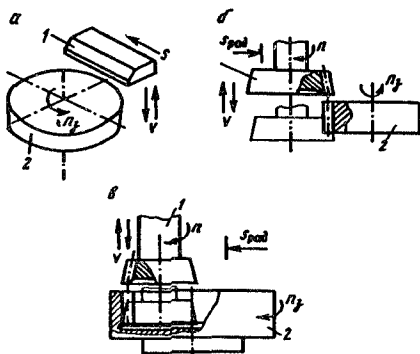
Схемы обработки зубьев цилиндрических зубчатых колес модульными долбяками: 1 — инструмент; 2 — заготовка
